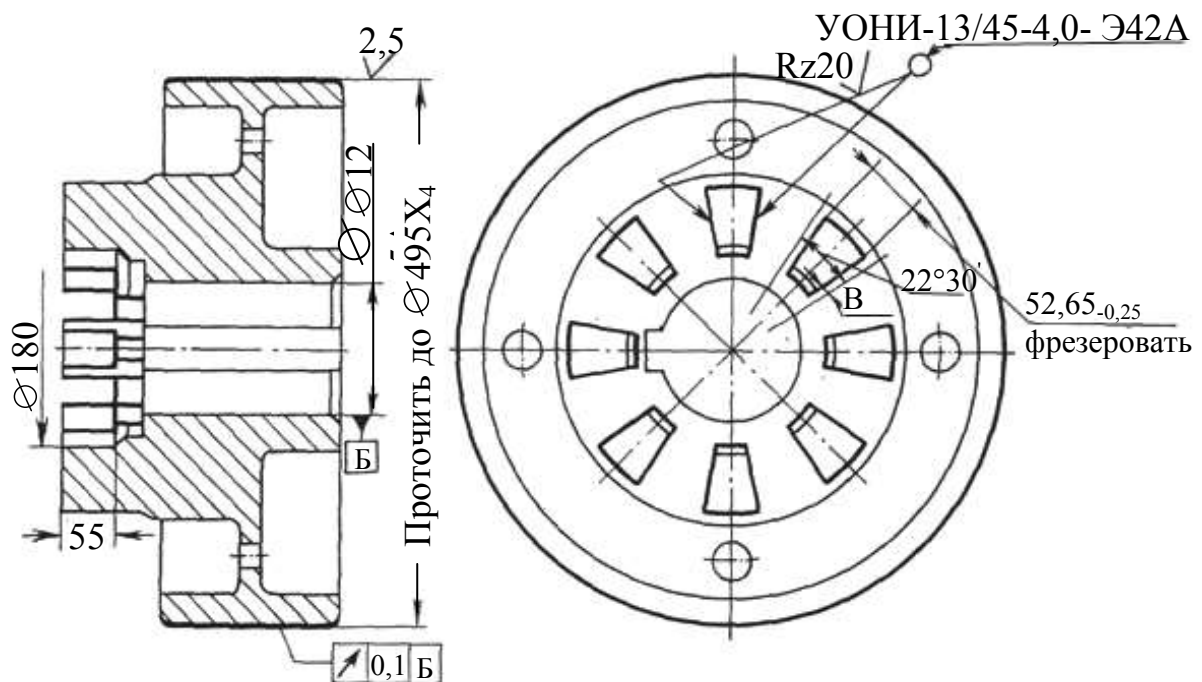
Ремонтный чертеж тормозного шкива-полумуфты
